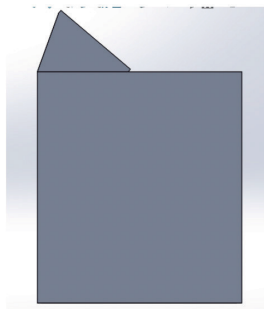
Caja donde estará el transformador en la máquina de soldadura por puntos, vista lateral derecha.
